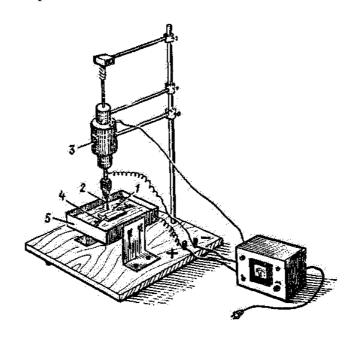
1 - обрабатываемая деталь; 2 - инструмент; 3 - электромагнитный вибратор; 4-зажимное устройство; 5-ванночка
